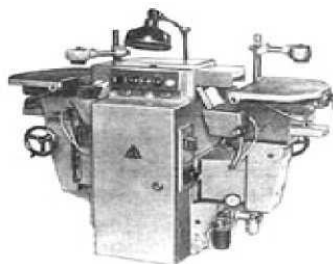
Верстат свердлильно-пазувальний СвПГ-2А
